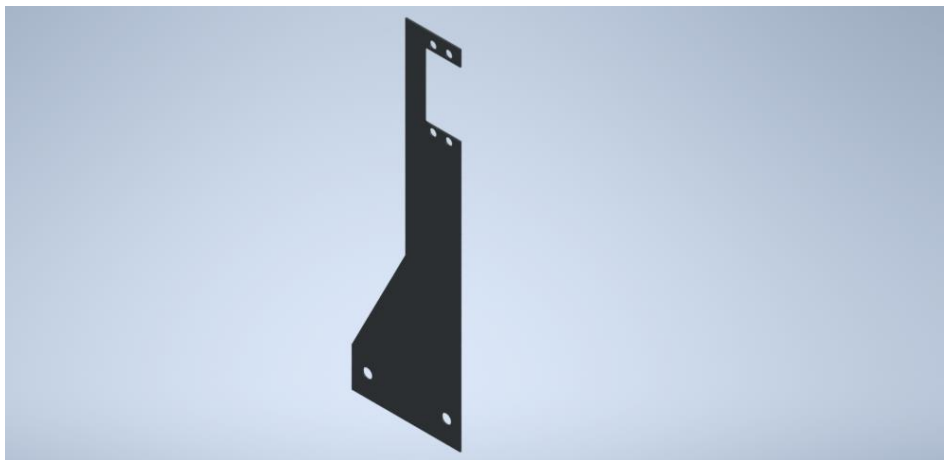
Diseño de placa soporte motor a pasos. (Autores)
